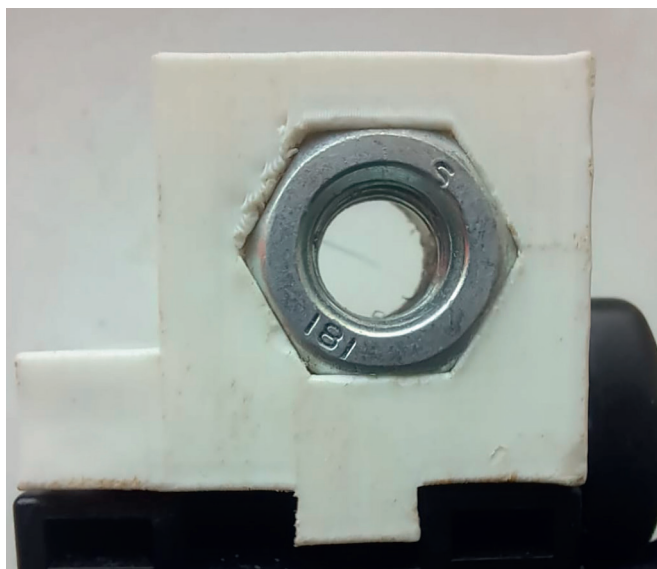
Металлические резьбовые вставки для пластмассовых деталей
